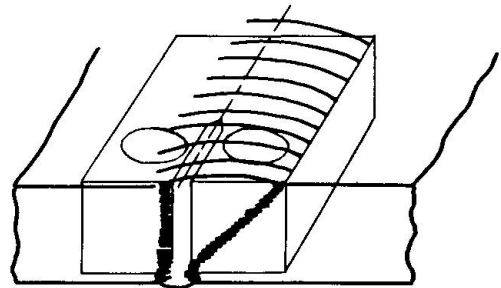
Prélèvement des éprouvettes dans les joints soudés bout à bout
